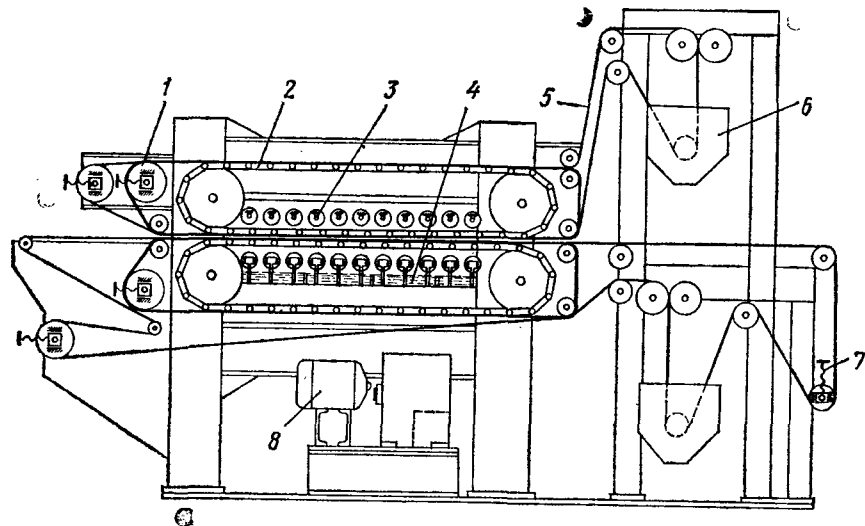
Устройство машины для непрерывной прессовки свеженамазанных пластин:
